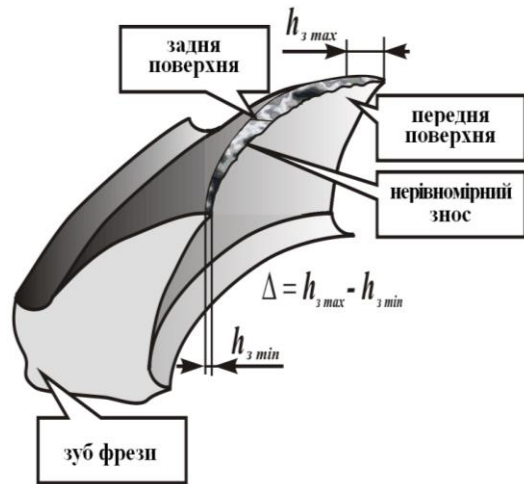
Схема нерівномірного зносу задньої поверхні зубця фрези по довжині ріжучої кромки
